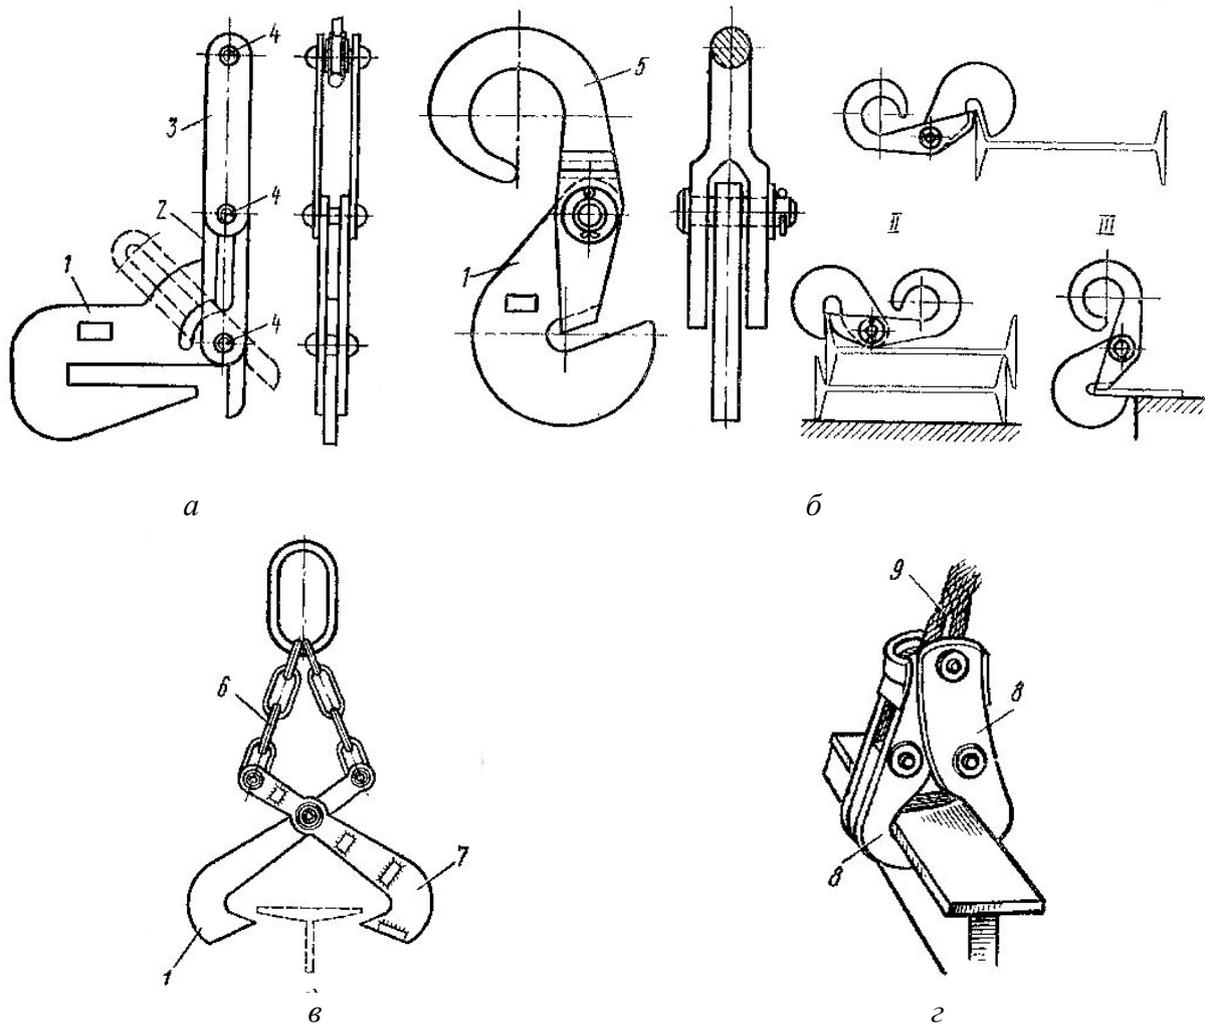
Универсальные захваты: *a* – захваты для подъема уголков и швеллеров, *б* – захваты для подъема профильного металла; *в*, *г* – захваты для подъема двутавровых балок: 1, 7, 8 – грузозахватные скобы; 2 – запорная серьга; 3 – тяга с роликами; 4 – оси шарниров; 5 – рычаг; 6 – строп; 9 – канат; I – II – III – примеры крепления захвата к конструкциям
